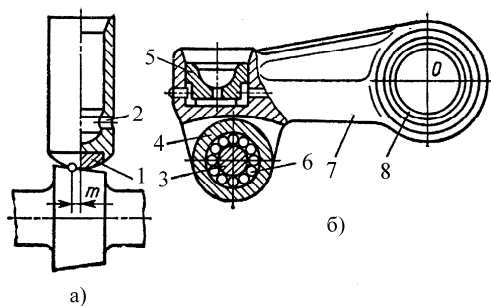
Типы толкателей: а – цилиндрический; б – рычажно-роликовый; 1 – наплавка; 2 – дренажное отверстие; 3 – ось ролика; 4 – ролик; 5 – пята; 6 – игольчатый подшипник; 7 – рычаг; 8 – втулка рычага
